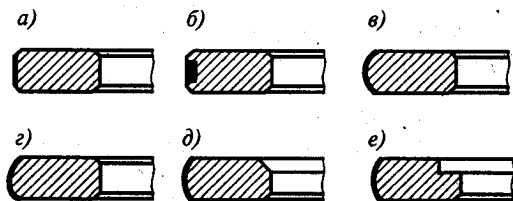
Профили верхних компресссионных колец двигателей легковых автомобилей:
